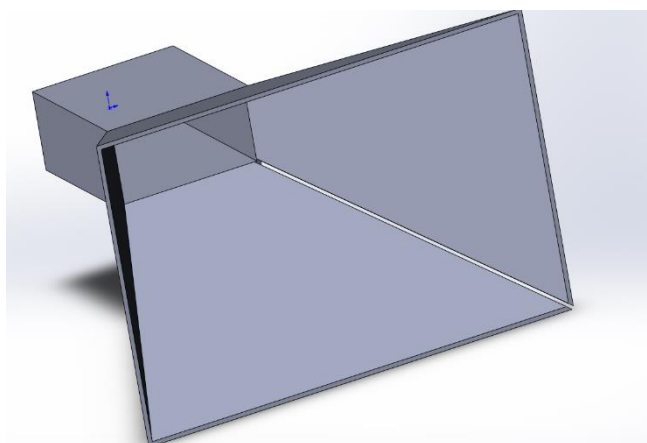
Модель рупора с нарушением сварного шва на раскрыве.
